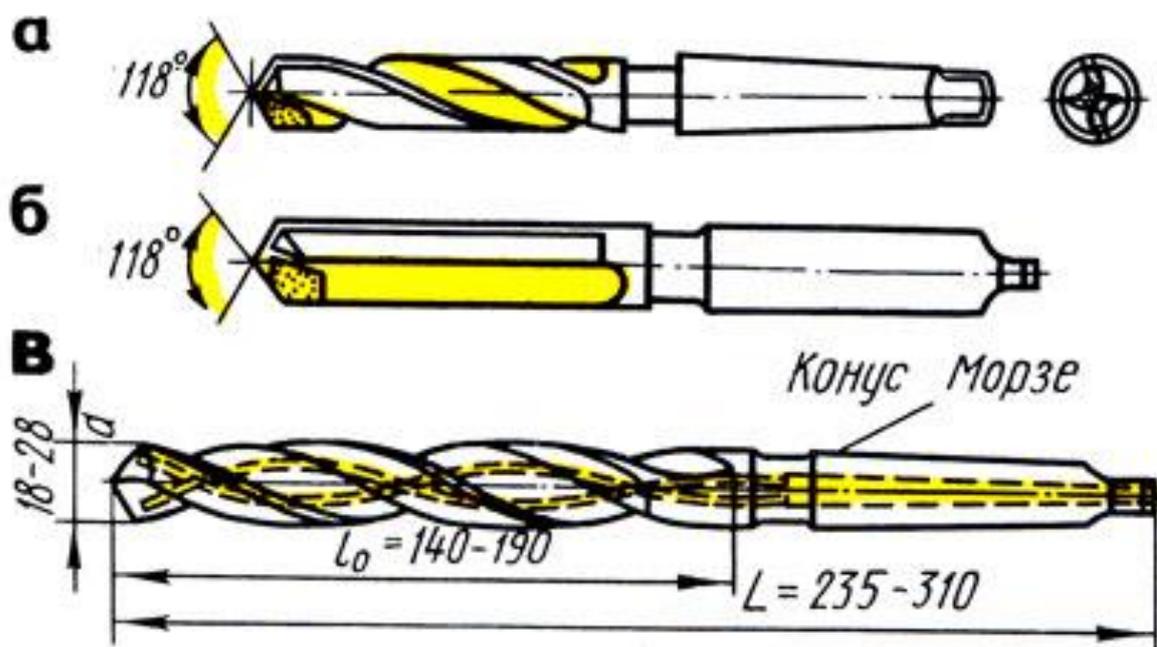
Сверла, оснащенные пластинками из твердого сплава с винтовыми (а), прямыми (б) канавками, каналами для охлаждающей жидкости (в)
